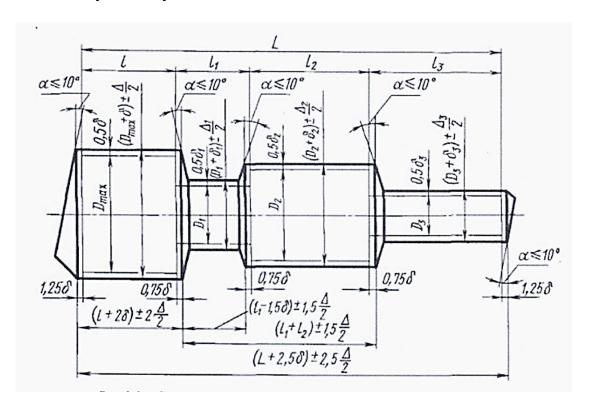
Припуски и допуски по длине и диаметрам ступенчатого вала
